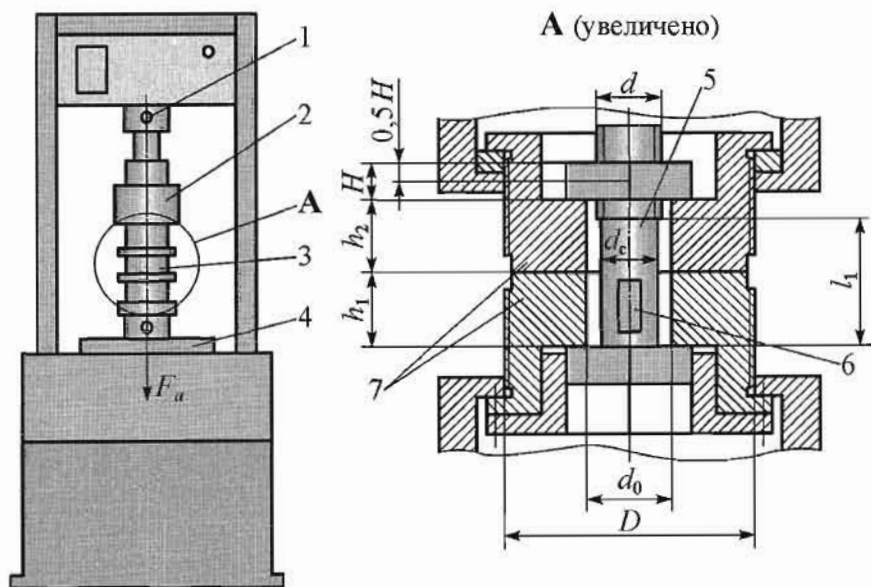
Схема универсальной испытательной машины с приспособлением ДМ-22А
